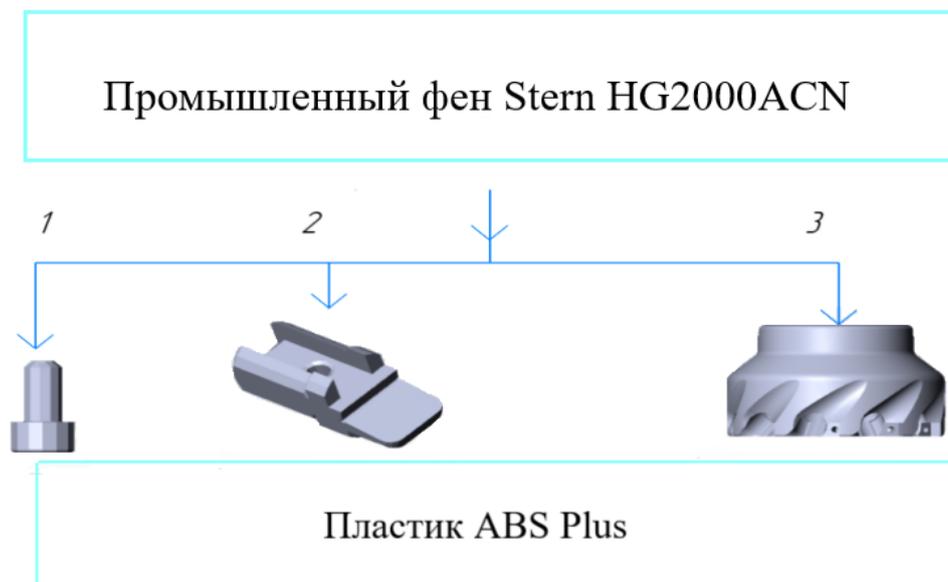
Схема проведения эксперимента: 1 – винт; 2 – корпус блока; 3 – корпус фрезы торцовой
